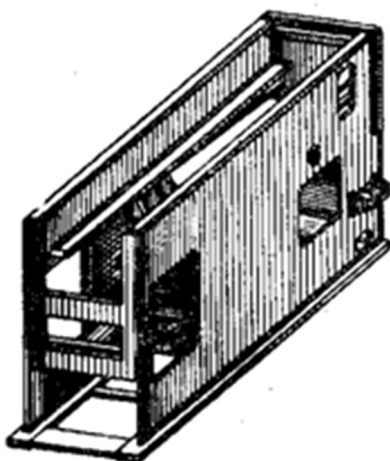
Сварная станина горизонтального протяжного станка, изготовленная на поточной линии
